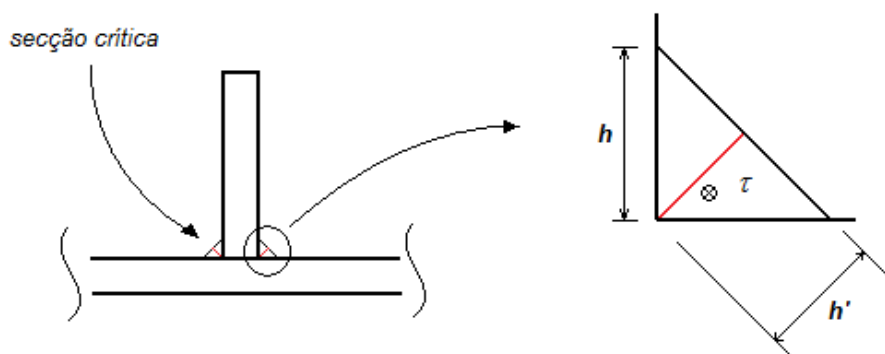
Esquema da ligação soldada e cordão de soldadura
